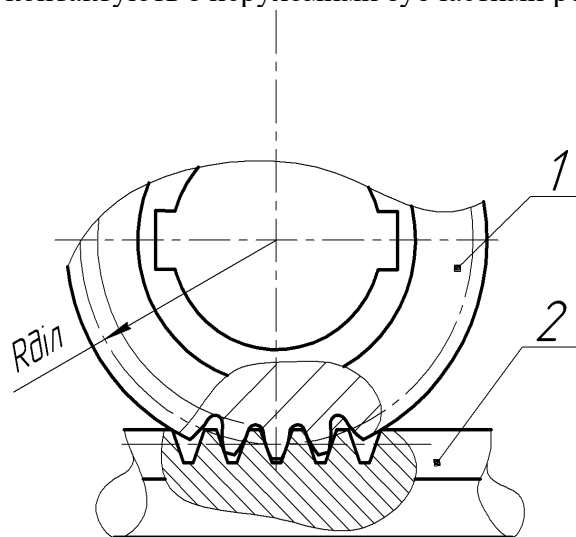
Ведуче зубчасте колесо та нерухома рейка станів холодної прокатки труб валками: 1 - валок; 2 – зубчата рейка;  $R_{dir}$ - дільний радіус ведучого зубчастого колеса
